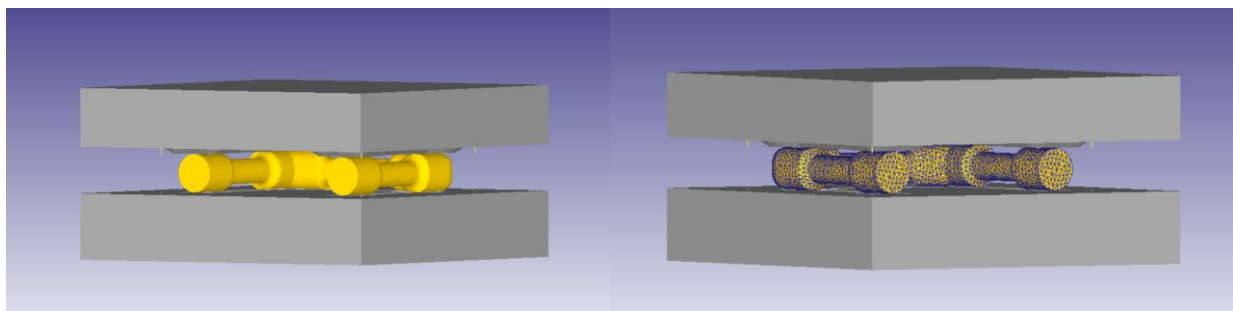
Генерування сітки для зігнутої заготовки
